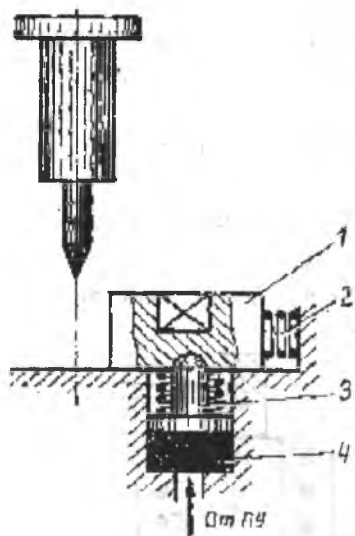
Принципиальная схема МДВ: 1- движок; 2- пружина; 3-- стопор; 4- запрессовка
